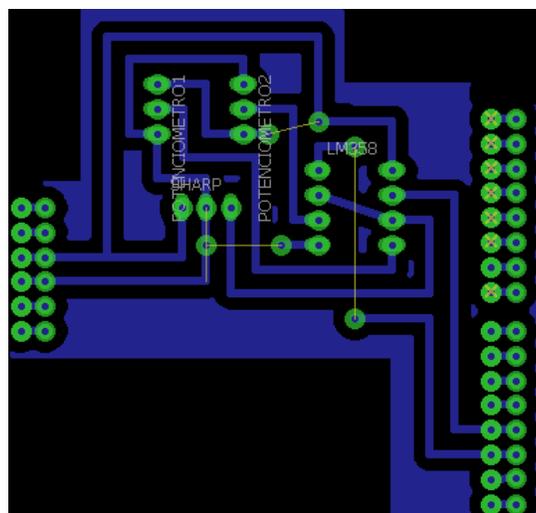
Diseño de la PCB - Shield para el sensor infrarrojo.
